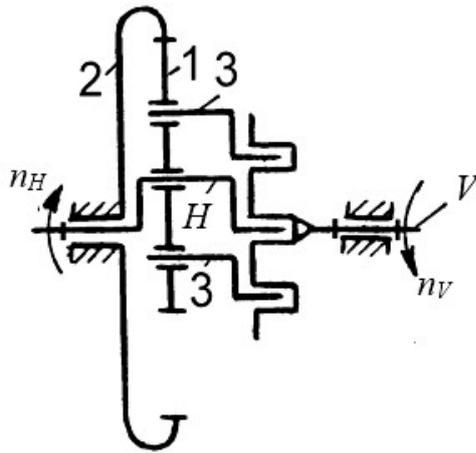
Планетарный механизм с параллельными кривошипами (схема $K-H-V$)
